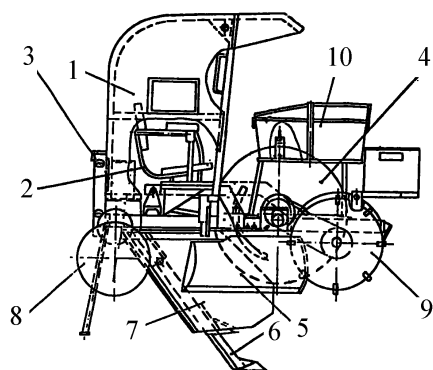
Схема лесопосадочной машины МЛУ-1А: 1 – кузов; 2 – сидение; 3 – рама; 4 – дисковый посадочный аппарат; 5 – дерносор; 6 – глубокорыхлитель; 7 – сошник; 8 – опорные колеса; 9 – прикатывающе-приводной каток; 10 – ящик для посадочного материала
